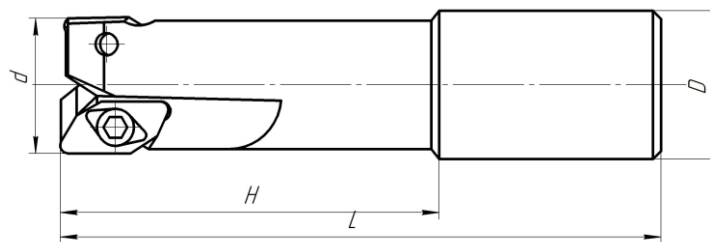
Кінцева фреза НМ90 EAL-D25-C24L180-16
